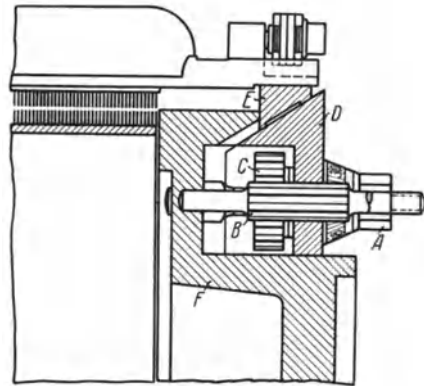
Einstellvorrichtung für die Deckellaufbahn von Krempeln mit wandernden Deckeln (Howard & Bullough Ltd., Accrington).
